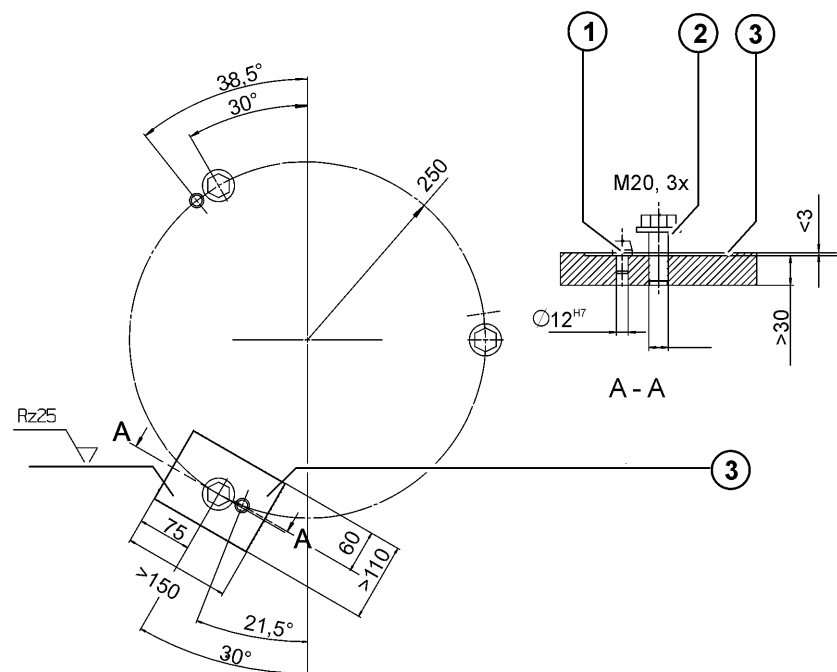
Maschinengestellbefestigung, Maßzeichnung
